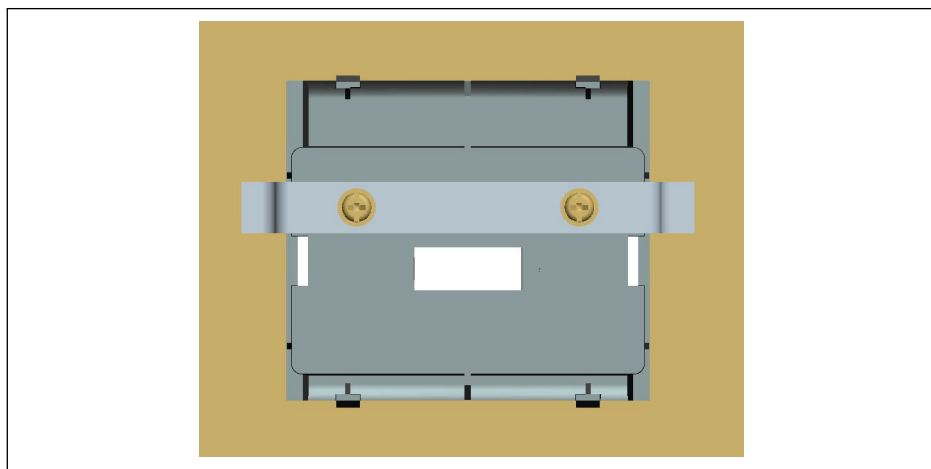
Fixer la plaque de montage (vue arrière)
